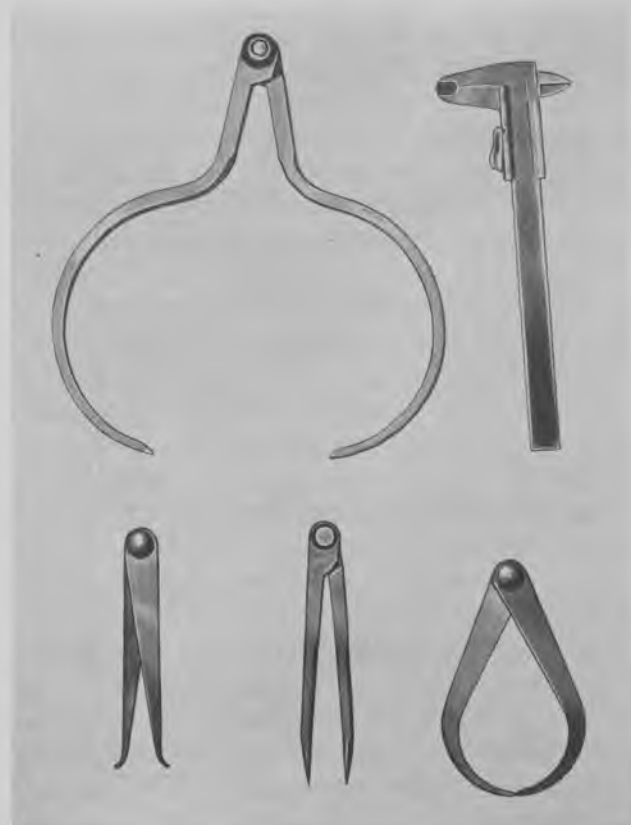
Krumpasser, skydemål, passer for måltagning i huller, retpasser og krumpasser.
